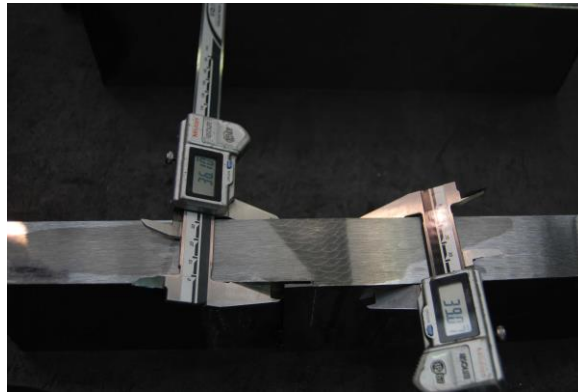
Ejemplo de desalineamiento en e cupón de soldadura para fractura
